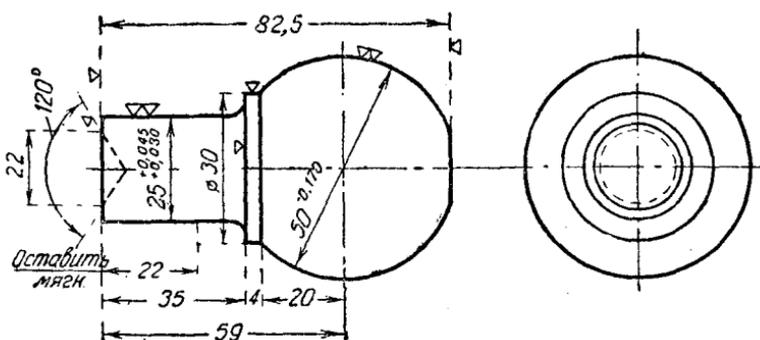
Дет. 18. Шаровой палец распорной тяги
